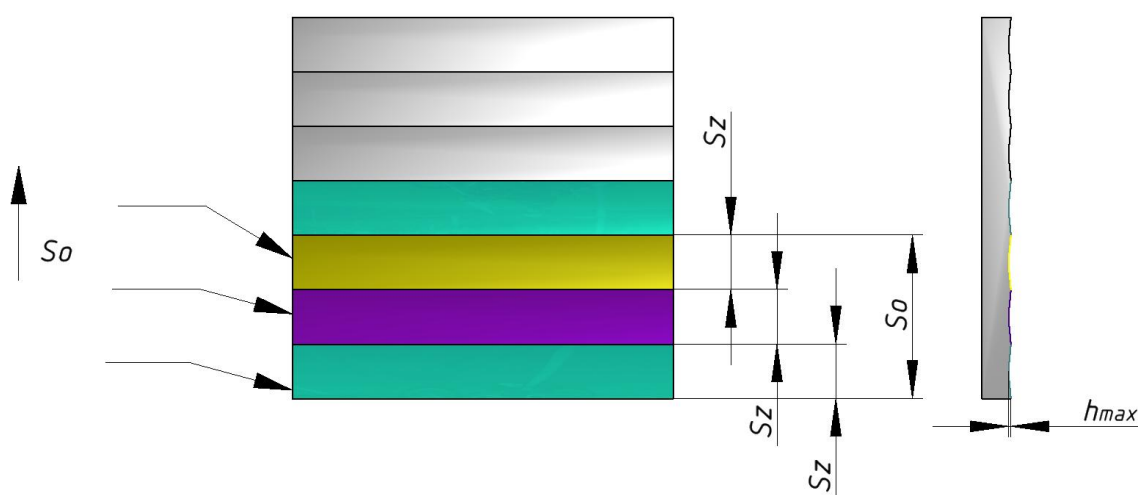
Вид поверхности, образованной фрезой с «гладкой» режущей кромкой
